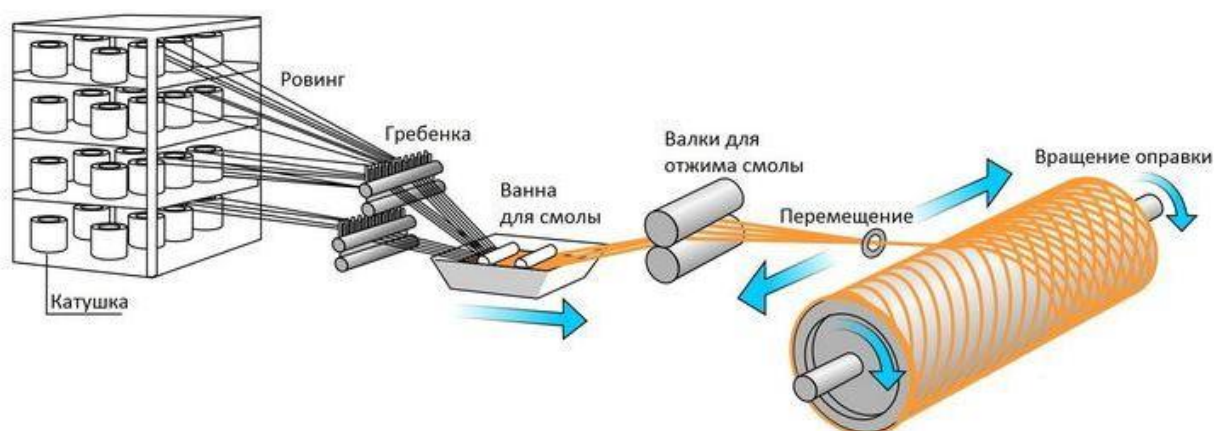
Процесс намотки стеклопластикового корпуса.
